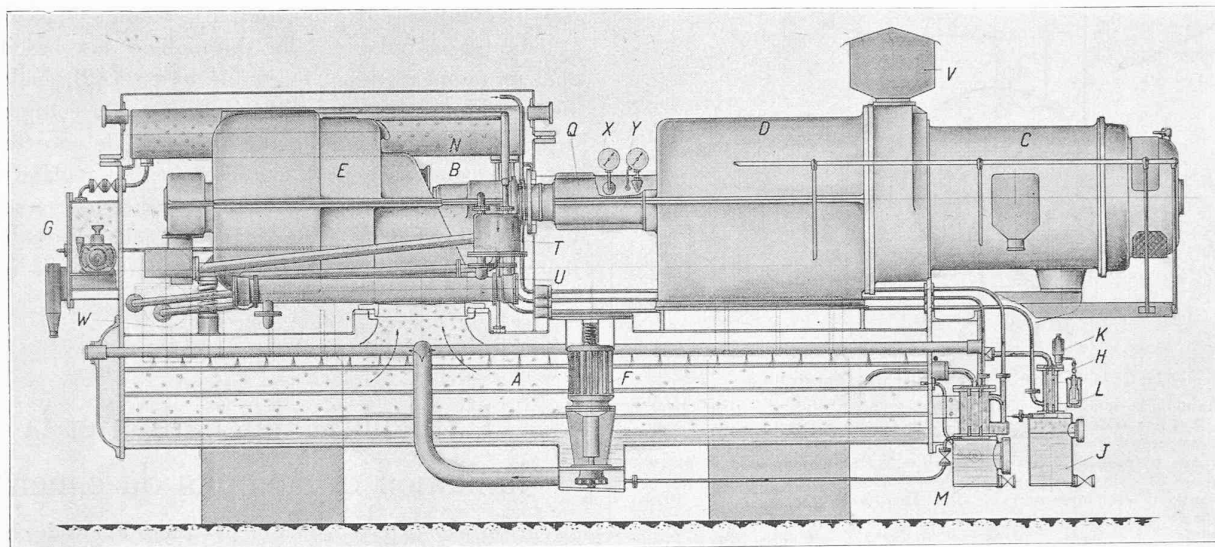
Vue d'ensemble du thermobloc BBC.
